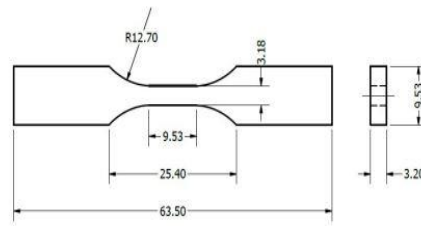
Geometría y dimensiones de la probeta para ensayo de tracción. Fuente: [10].
